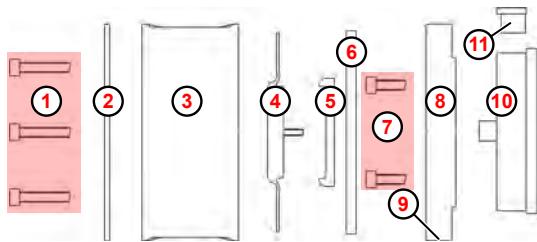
Remplacement de la membrane et de la partie supérieure de la pompe - type 00800 - 01200
